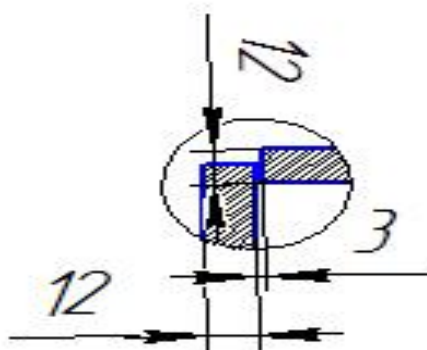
соединение под сварку Н1 ГОСТ 8713 -79
